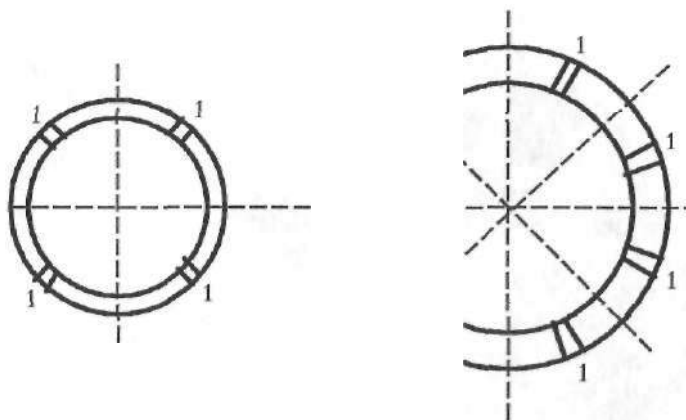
Схема вырезки образцов для испытаний при аттестации сварщиков:
